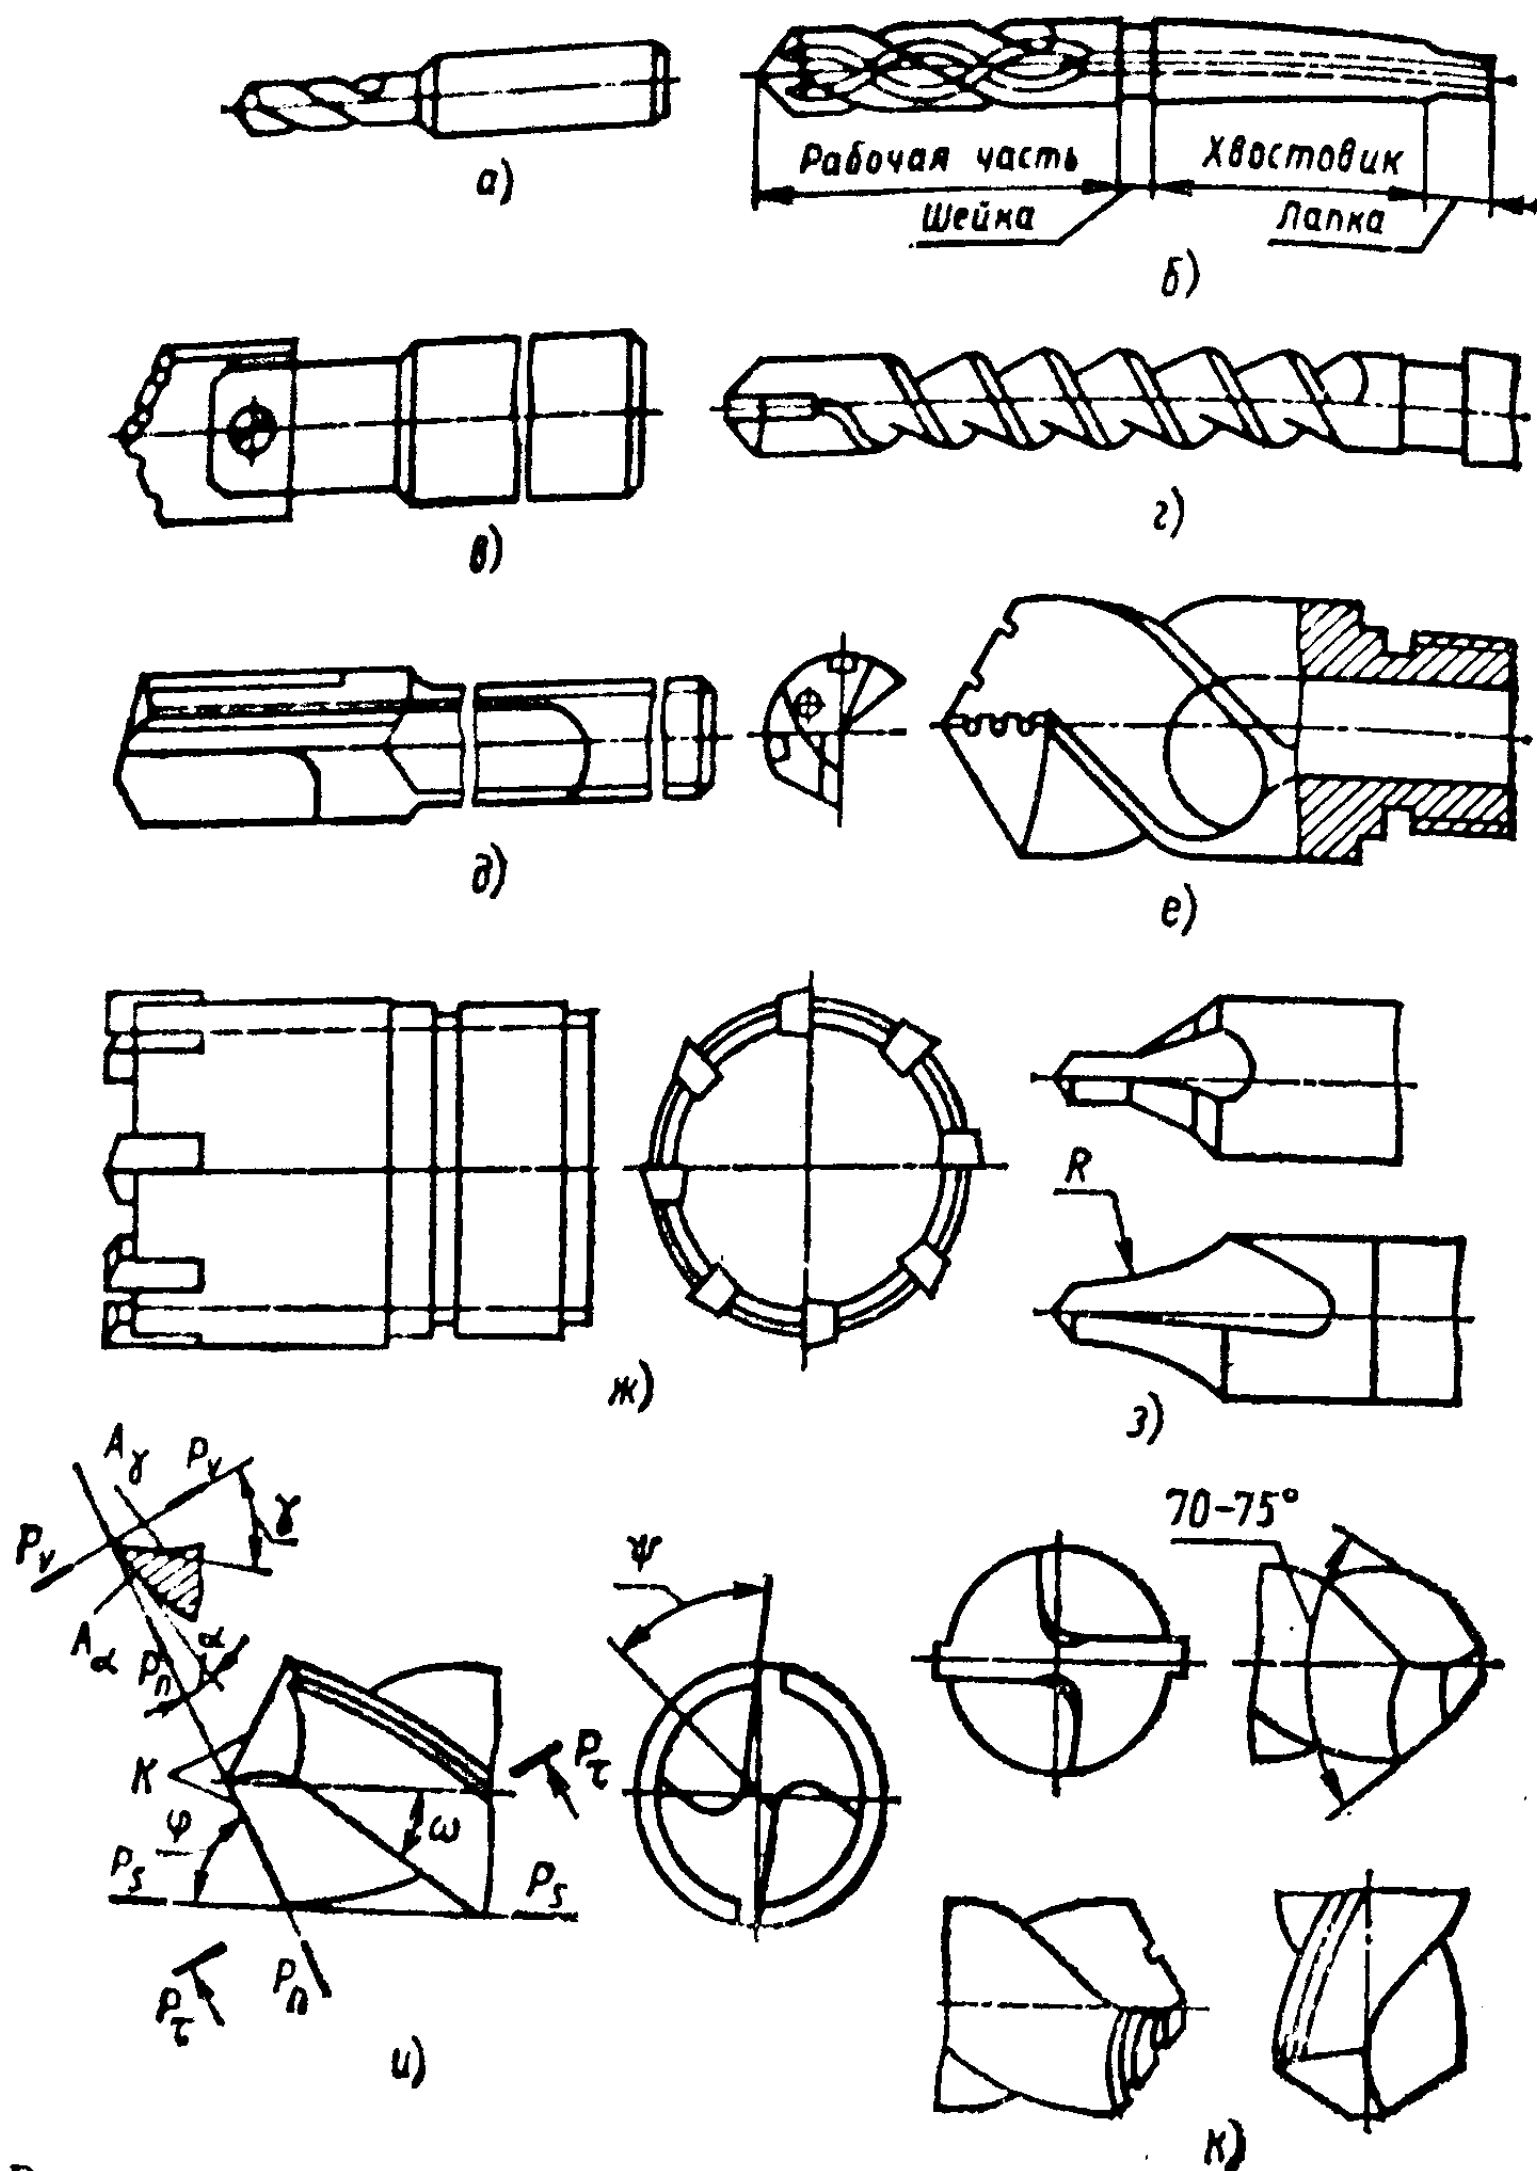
,1. Конструкции сверл (а—з), геометрические параметры режущей части (и) и формы заточки (к)
